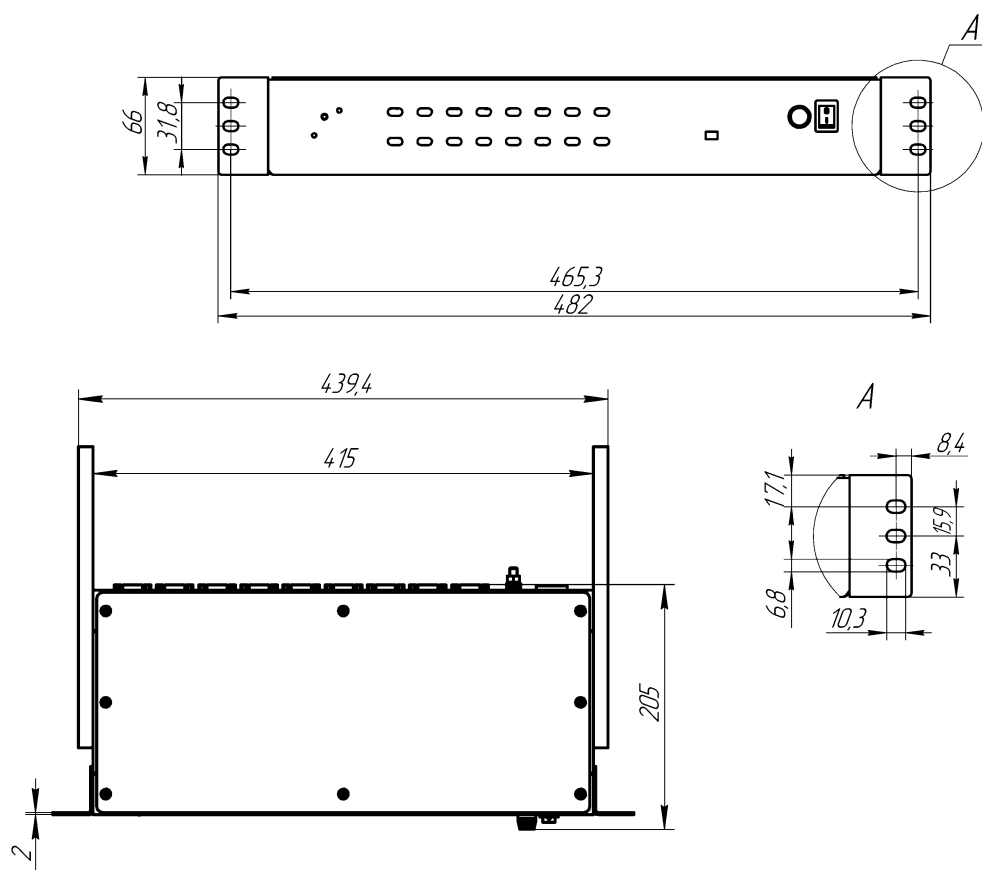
Габаритные размеры КУВВ-143-116
